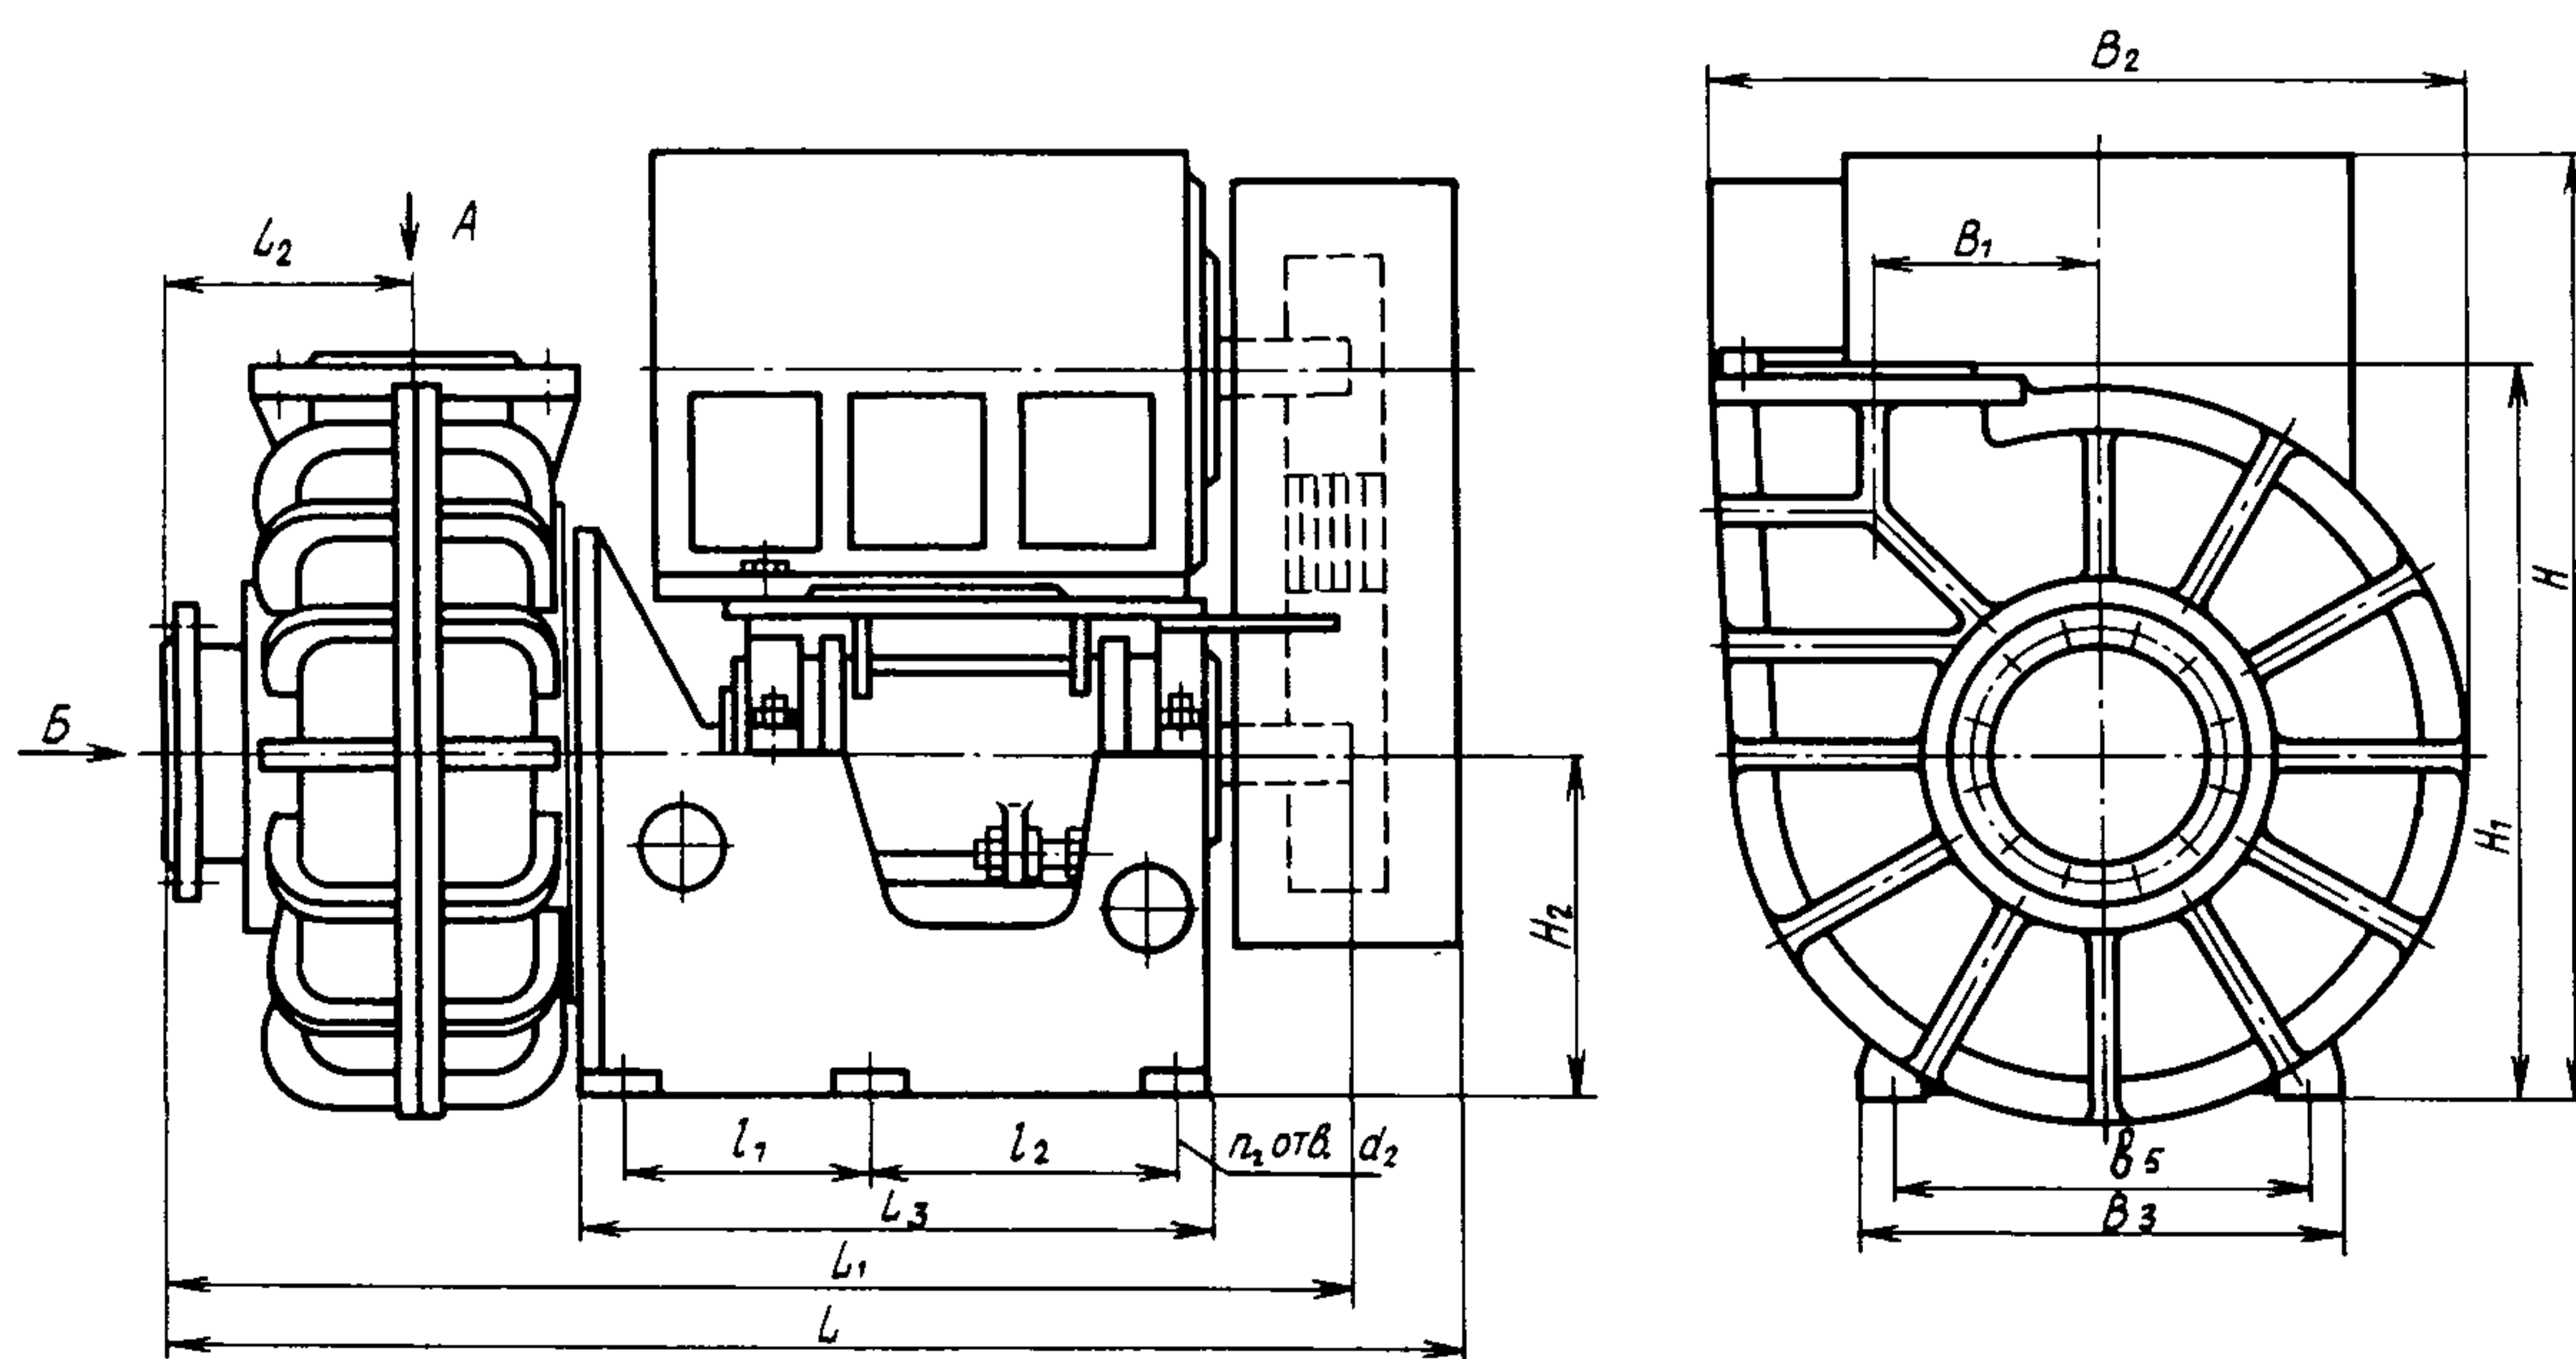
Габаритный чертеж электронасосного агрегата типа ГрА с приводом через клиноременную передачу (верхнее расположение электродвигателя)
